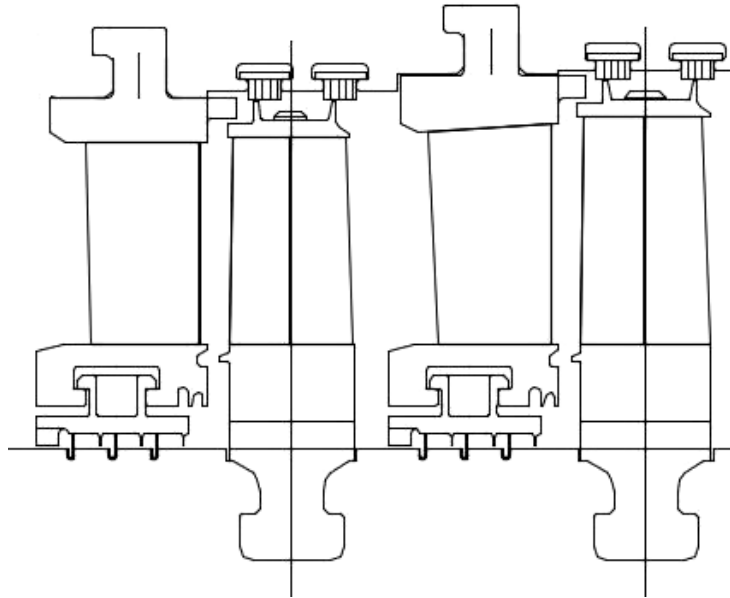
Přetlakový stupeň s bubnovou konstrukcí rotoru
